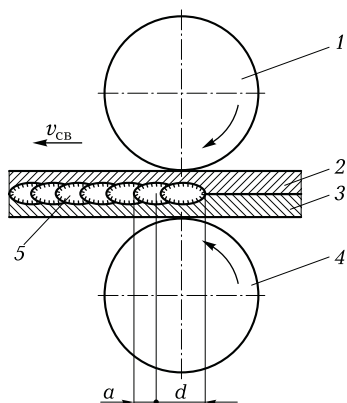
Схема процесса контактной шовной сварки:
